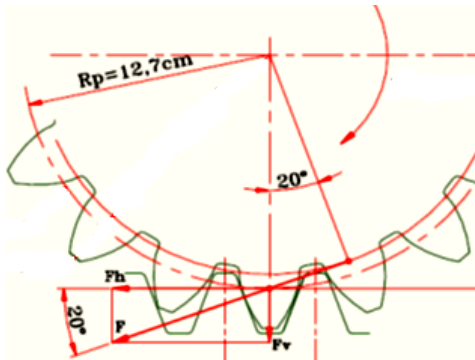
Engranaje del piñón motriz y la cremallera perimetral del carousel. Fuerzas aplicadas.
